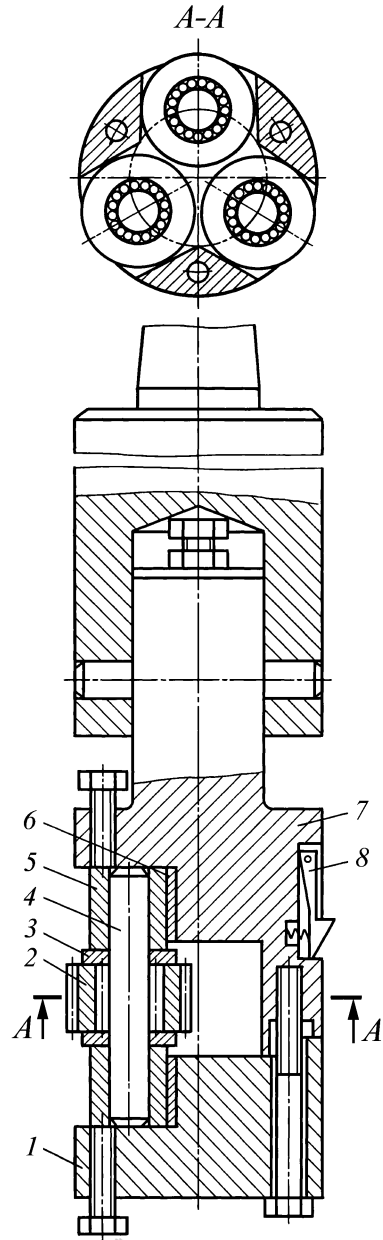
Резьбонакатная головка для накатывания цилиндрических резьб:
